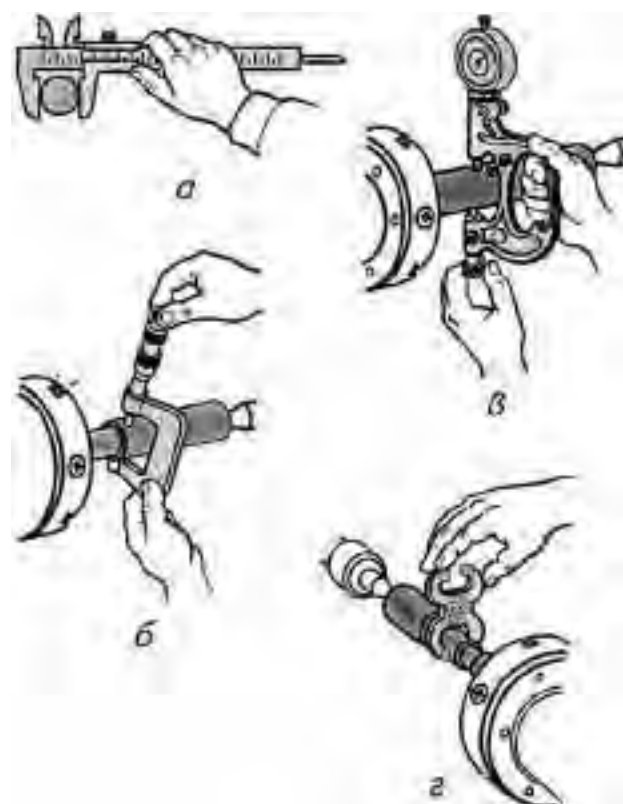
КОНТРОЛЬ ДІАМЕТРА ЗАГОТОВКИ (ДЕТАЛІ)
